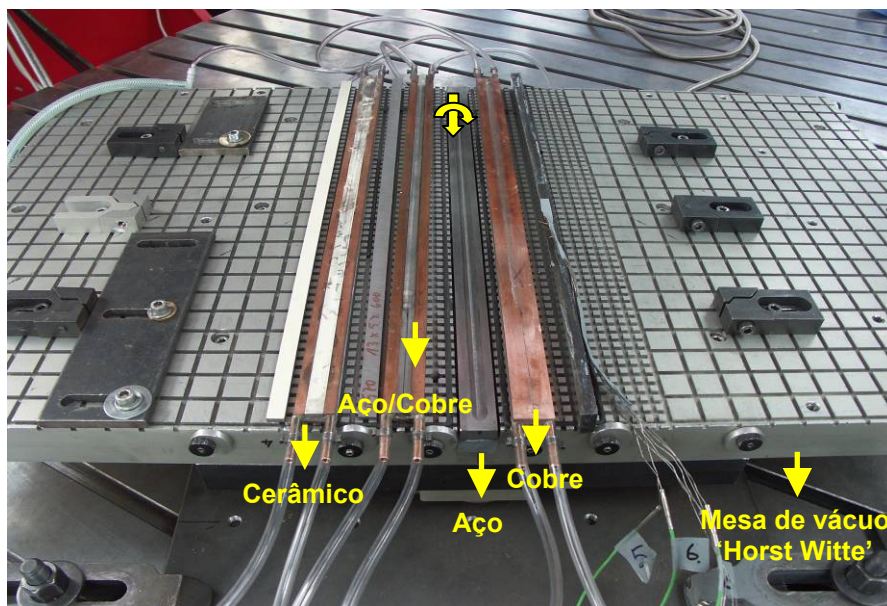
Backing* de diferentes materiais utilizados durante o processo FSW sob a mesa com sistema de fixação mecânica e a vácuo das chapas soldadas.
